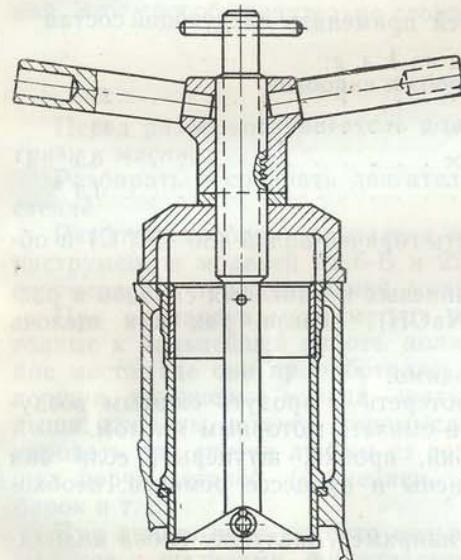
Съемник для выпрессовки гильзы цилиндра
